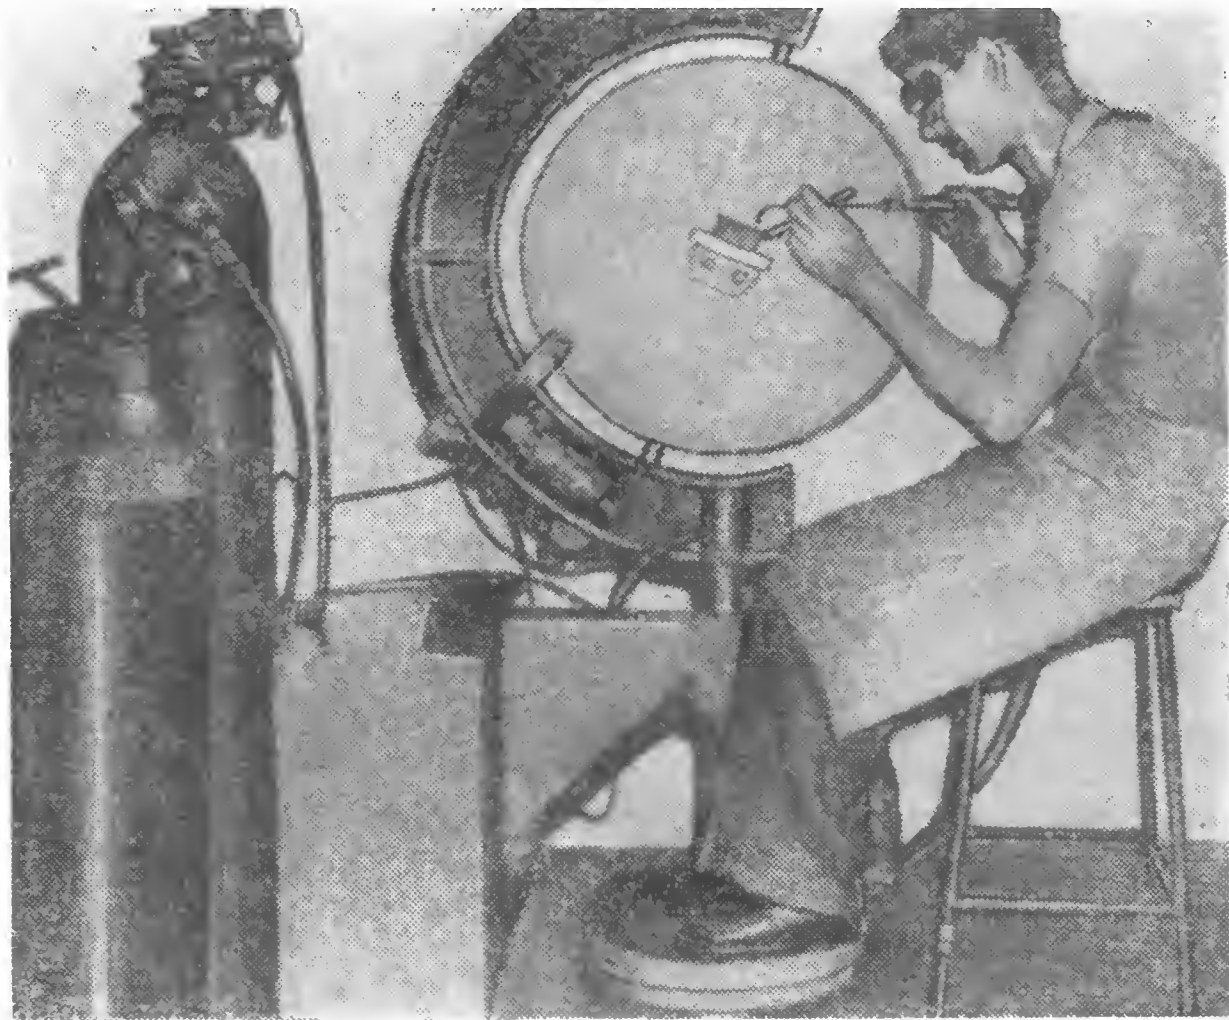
Работа на приспособлении для сварки мелких деталей
